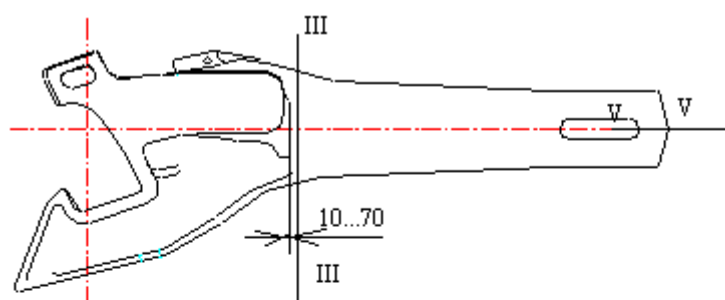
Места порезки корпуса автосцепки для контроля внутренних дефектов
